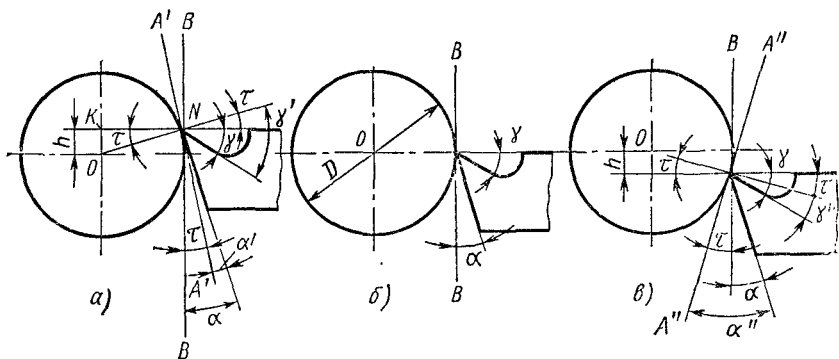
Влияние установки вершины реза по отношению к оси заготовки на углы
